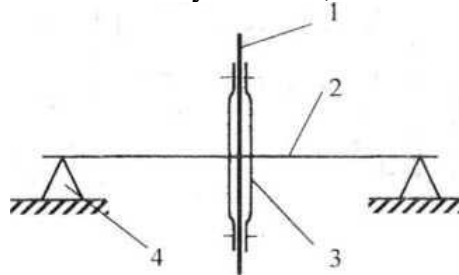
Схема установки для балансування дисків: 1 – диск; 2 – вал; 3 – планшайба; 4 - призма
